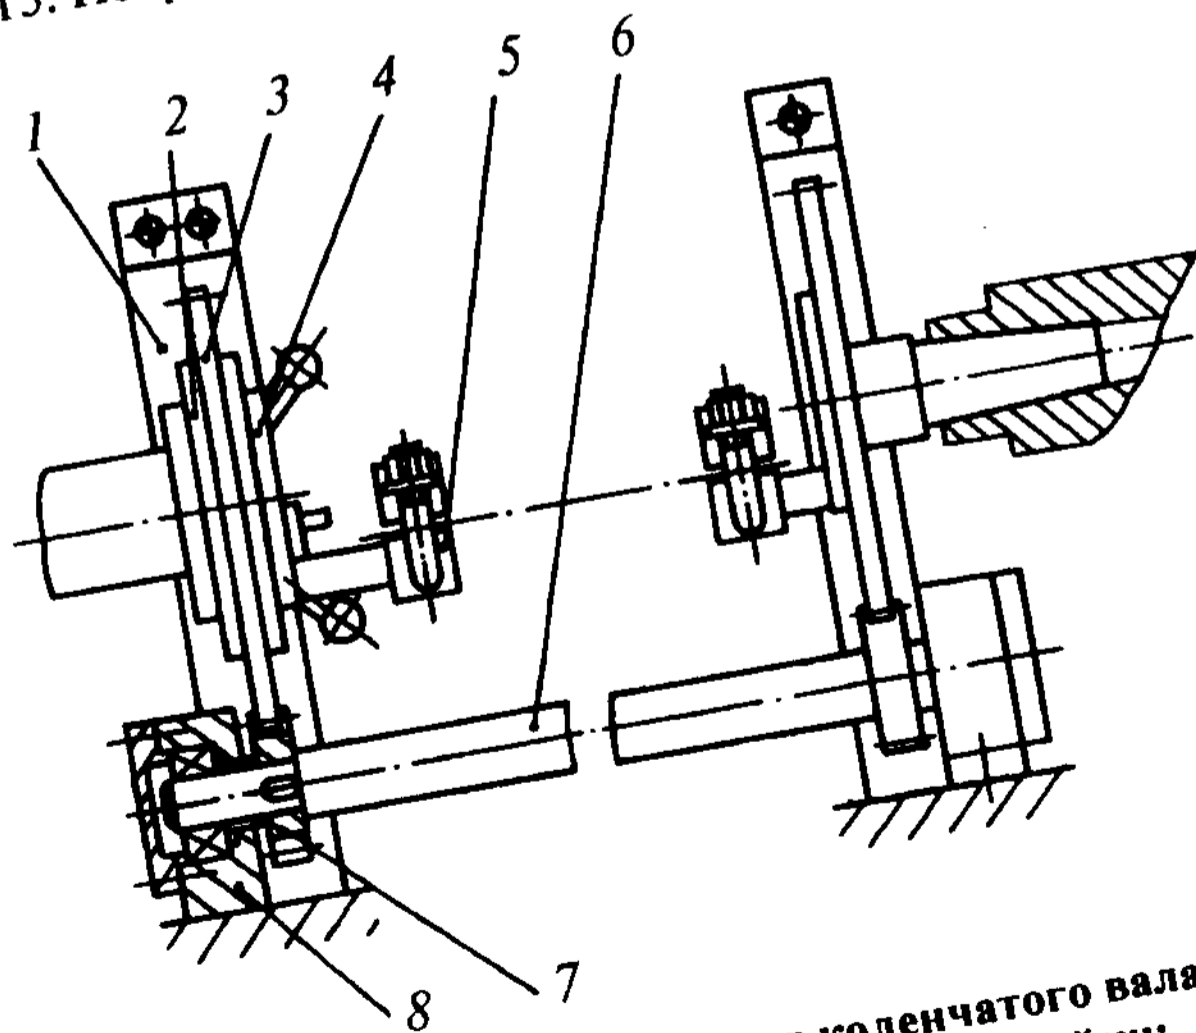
Схема вращателя коленчатого вала для напыления покрытий на его шейки:
